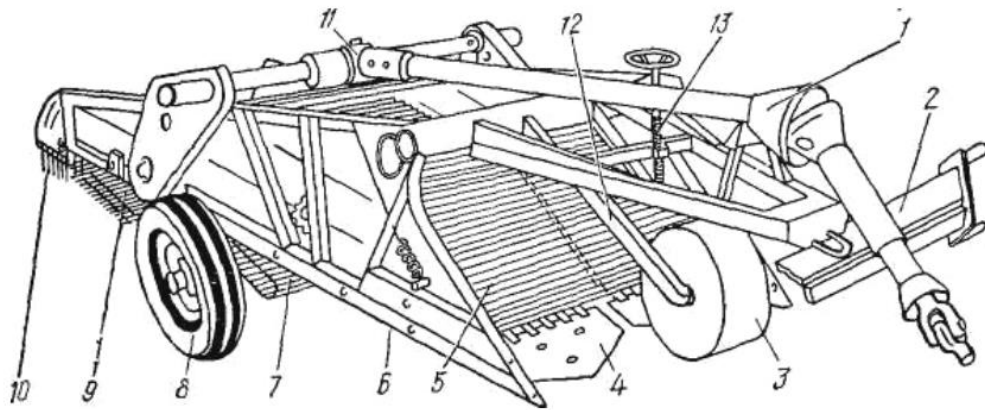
Картоплекопач швидкісний КСТ-1,4: 1 – карданна передача; 2 – поперечина начіпного пристрою; 3 – копіювальне колесо; 4 – леміш. 5 – швидкісний елеватор 6 –рама; 7 – основний елеватор; 8 – ходове колесо; 9 – каскадний елеватор; 10 – відбивач; 11 – редуктор; 12 – рамка копіювального колеса; 13 – гвинтовий механізм.
